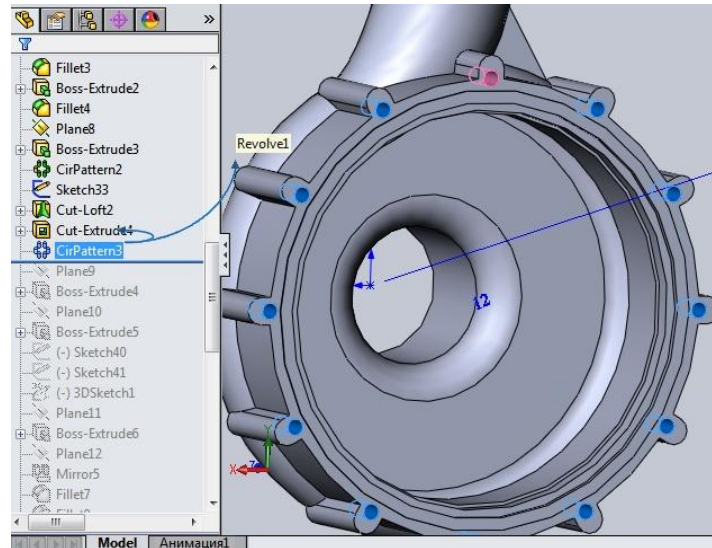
Отвори для кріплення кришки корпусу
